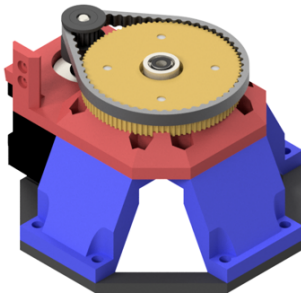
Sistema de banda de engranajes para el motor paso a paso base [Hecho en Inventor]
